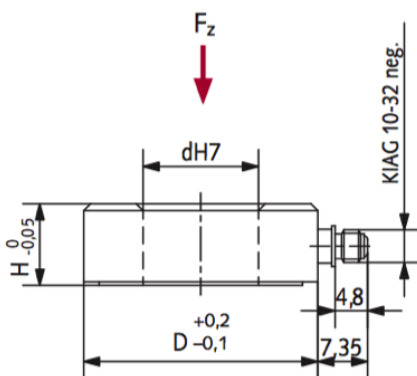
Dimensions rondelle de charge, Type 9001A ... 9031A
